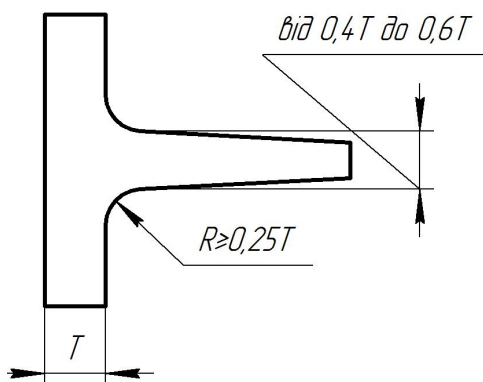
Загальні правила конструювання ребра для деталей ІЛП
